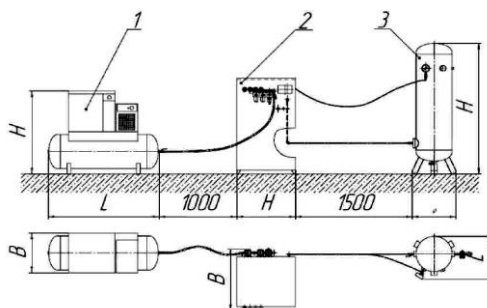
Кислородная установка «Провита»: 1 – воздушный компрессор; 2 – генератор кислорода; 3 – ресивер
